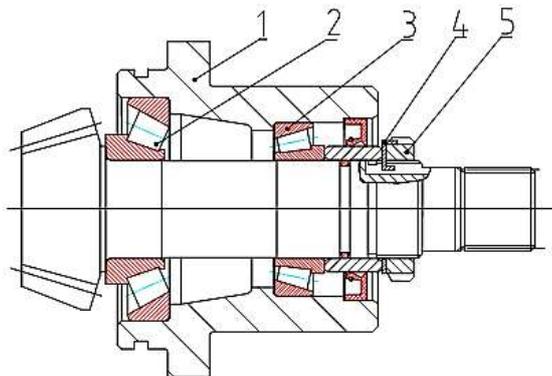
Регулировка подшипника ведущей конической шестерни переднего центрального привода.
